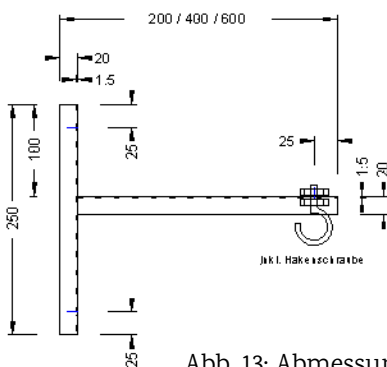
Abmessungen Wandausleger zur Installation von AquaCheck
